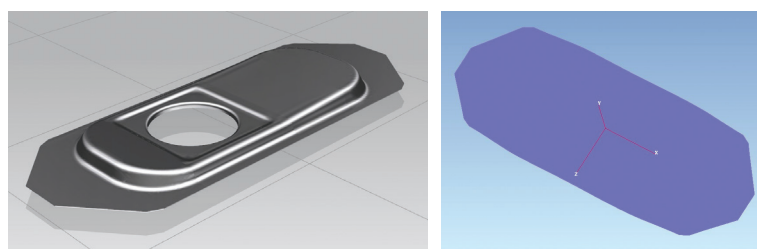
Модель детали типа «окантовка» и заготовки для нее
